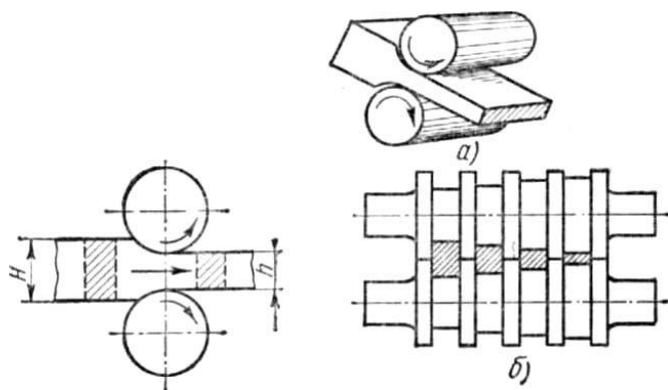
Схема прокатки металла с лева и с права валки для прокатки металла: а – листа; б – профилей.
